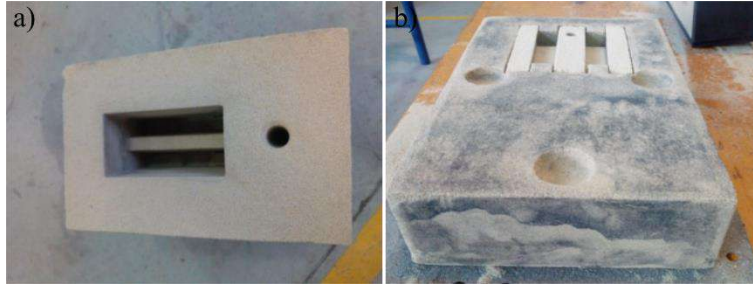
Molde terminado. a) Parte superior y b) Parte inferior.
